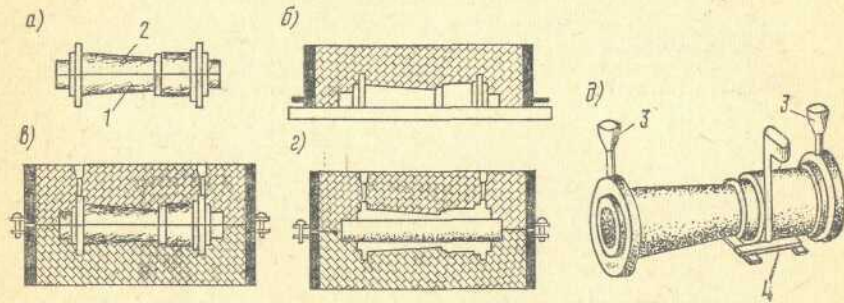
Изготовление отливки втулки по деревянной модели
